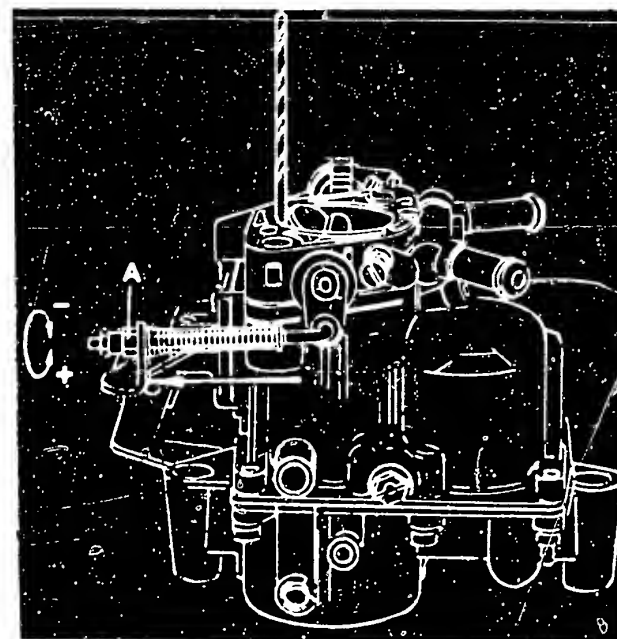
Einstellung des Beschleunigerpumpenhubes. Schraube A lösen, 2...4mm-Bohrer zwischen Drosselklappe und Gehäuse schieben und Schraube A bis zum Kontakt mit dem Hebel anziehen.
